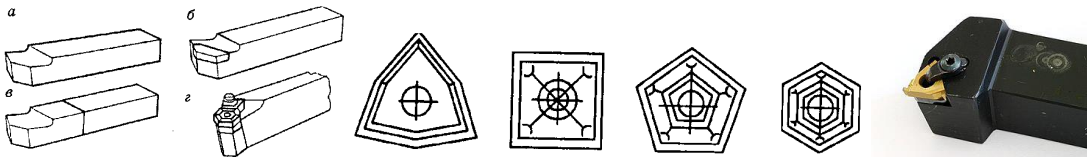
Типы токарных резцов по конструкции: цельные (а, б) составные с припаянными (в) или с механическим креплением (г) пластинами
